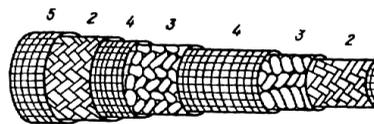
Конструкция рукава высокого давления с металлической оплеткой: 1 – внутренний резиновый слой; 2 – хлопчатобумажная оплетка; 3 – металлическая оплетка; 4 – резиновый слой; 5 – наружный резиновый слой
